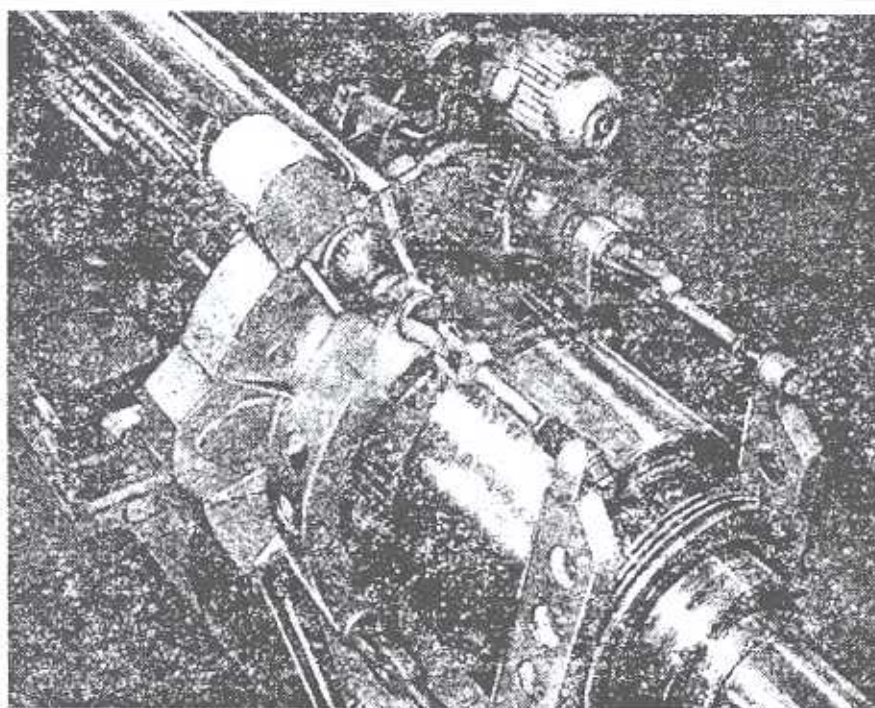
Машина для съема и надевания бандажей (положение для надевания; привод ходовых винтов – гидромоторами)
